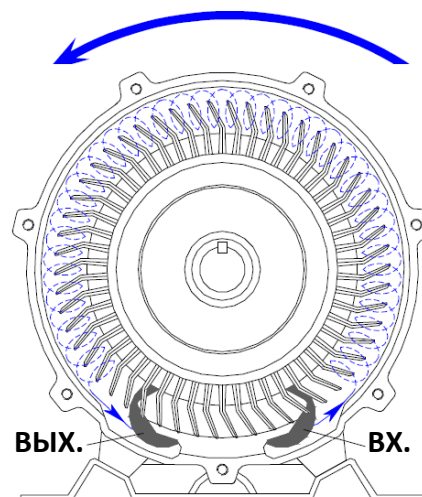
Вращение и движение воздуха по крыльчатке, если смотреть от крышки компрессора.
